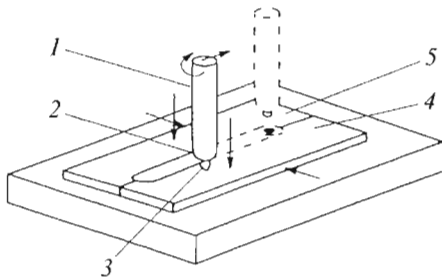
Технологическая схема процесса сварки трением с перемешиванием
